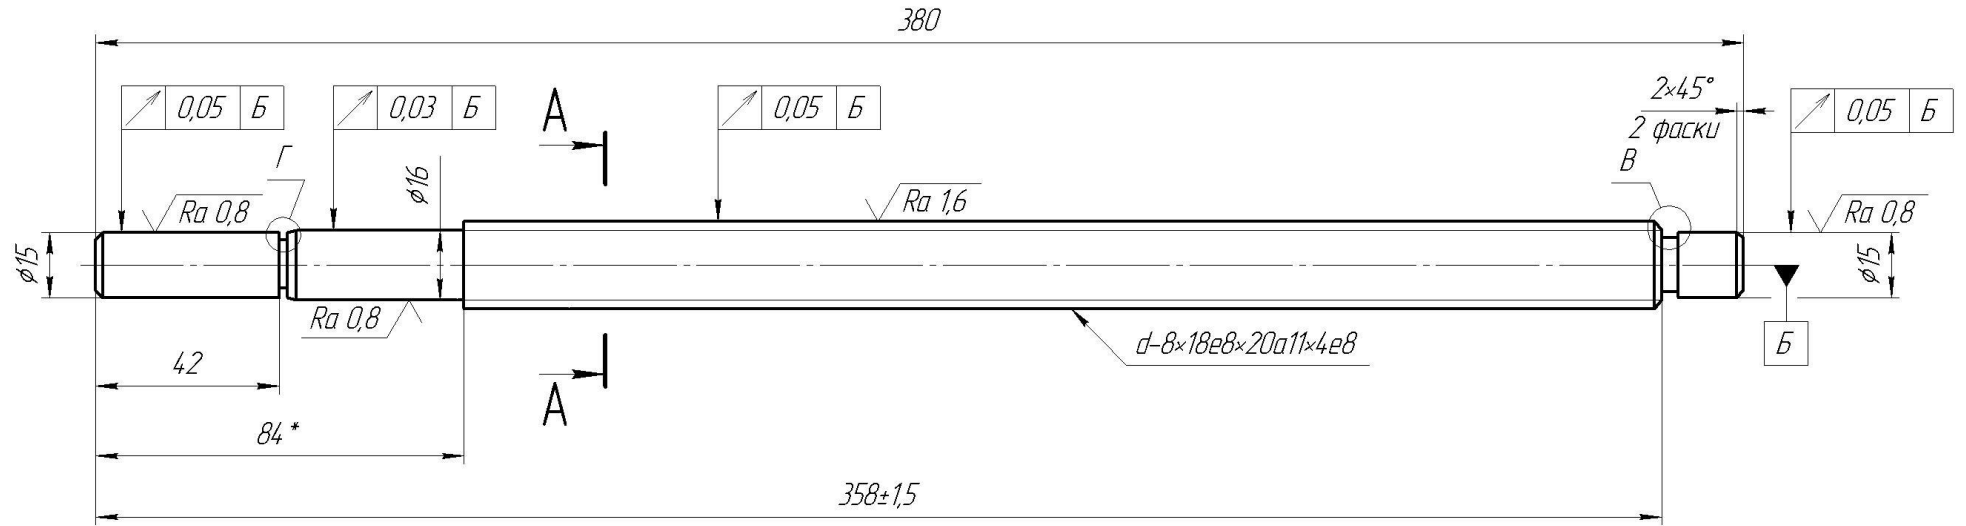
Кресленик деталі «Вал шліцьовий»
